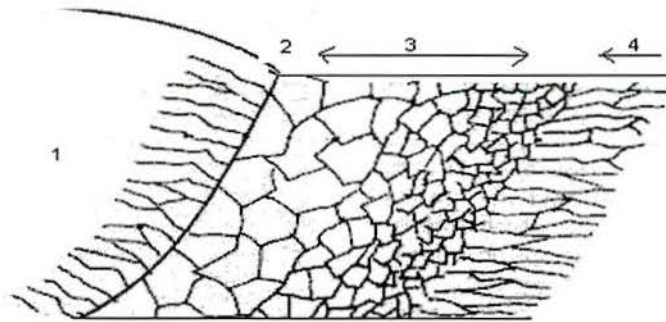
Regiões de uma junta soldada: 1) Metal de Solda; 2) Interface MS/ZAC; 3) Zona Afetada pelo Calor; 4) Metal base⁽³⁾
